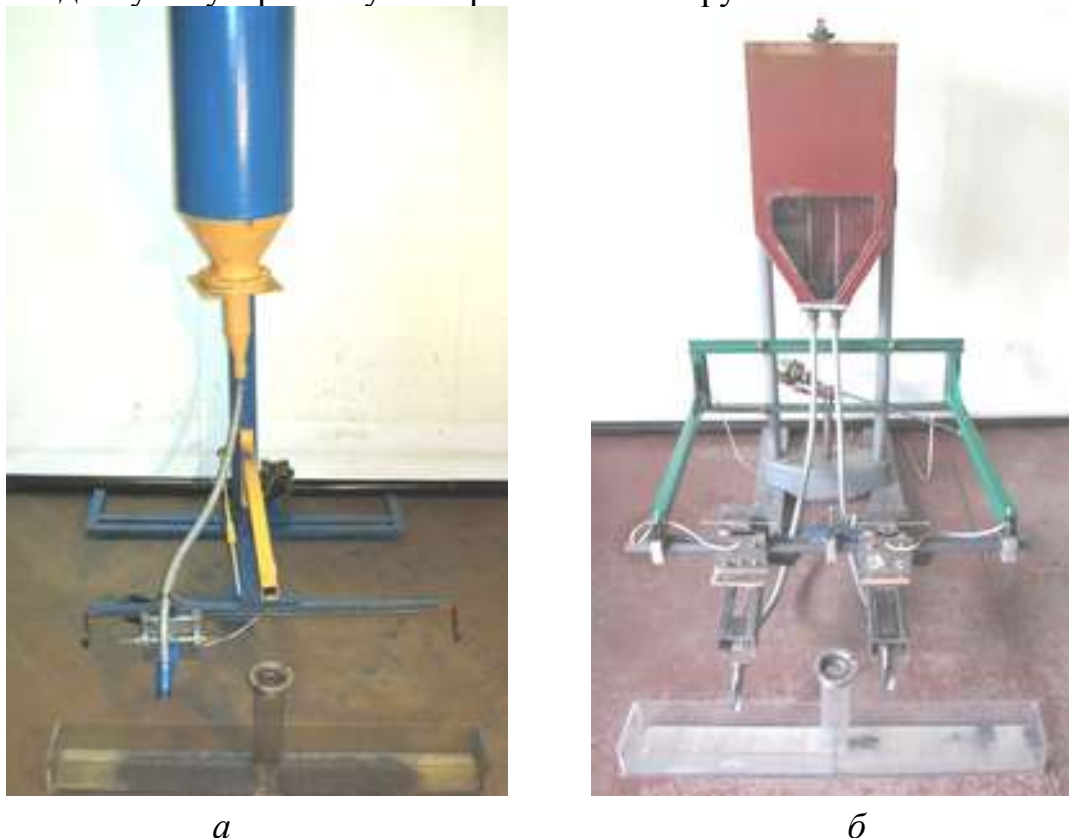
Опытные образцы систем нового поколения для реализации механизированной подачи ШОС в кристаллизаторы слябовых МНЛЗ для отливки заготовок крупного (а) и особо крупного (б) сечений
